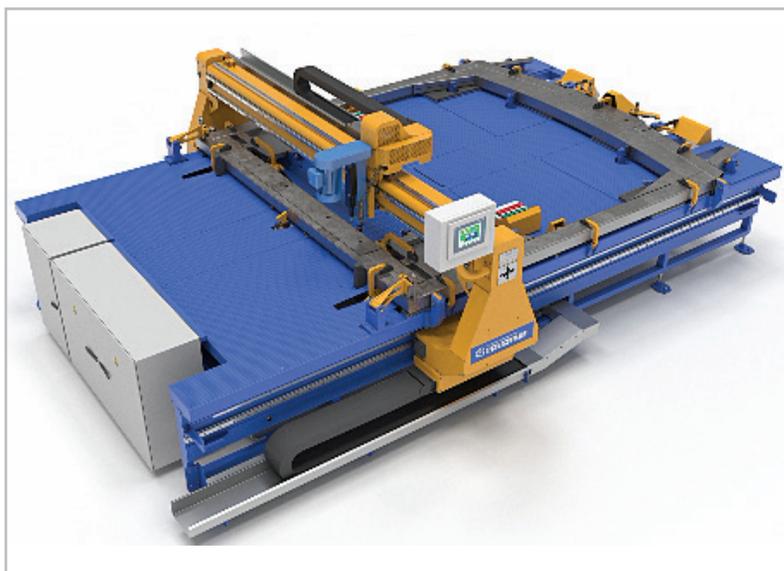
Общий вид стенда сварки и сверления рам соединения секций трамваев.
